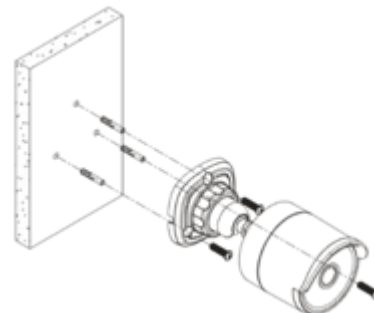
b Installare la telecamera a muro utilizzando opportuni supporti e viti in funzione del tipo di materiale del soffitto.
